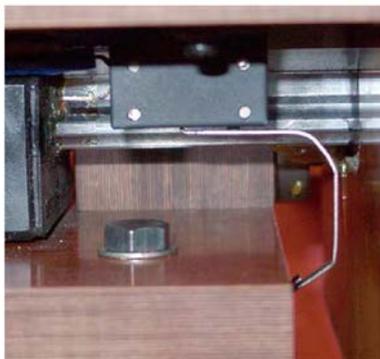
Стандартный концевой выключатель – миниатюрный выключатель установлен на столе и срабатывает при контакте со станиной станка.
